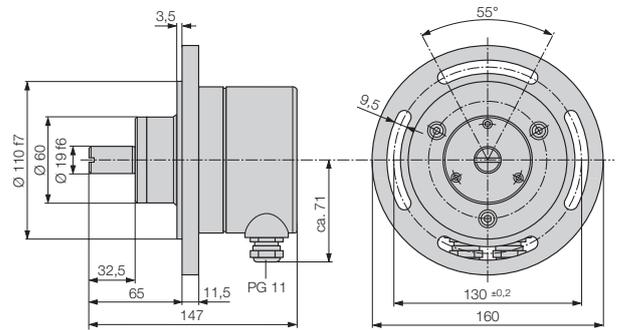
KINAX WT 707 avec bornes à vis, ainsi que presse-étoupes et flasque
